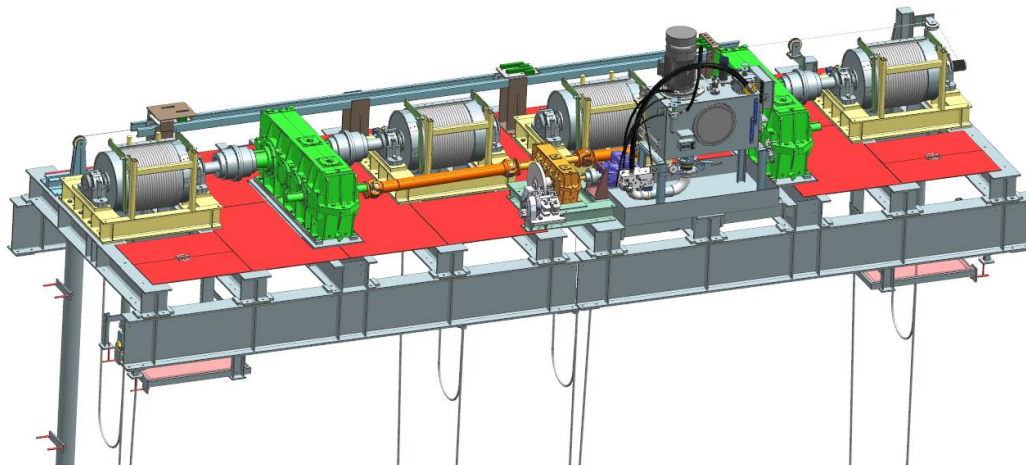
Vue d'amont vers l'aval d'ensemble d'un treuil double
